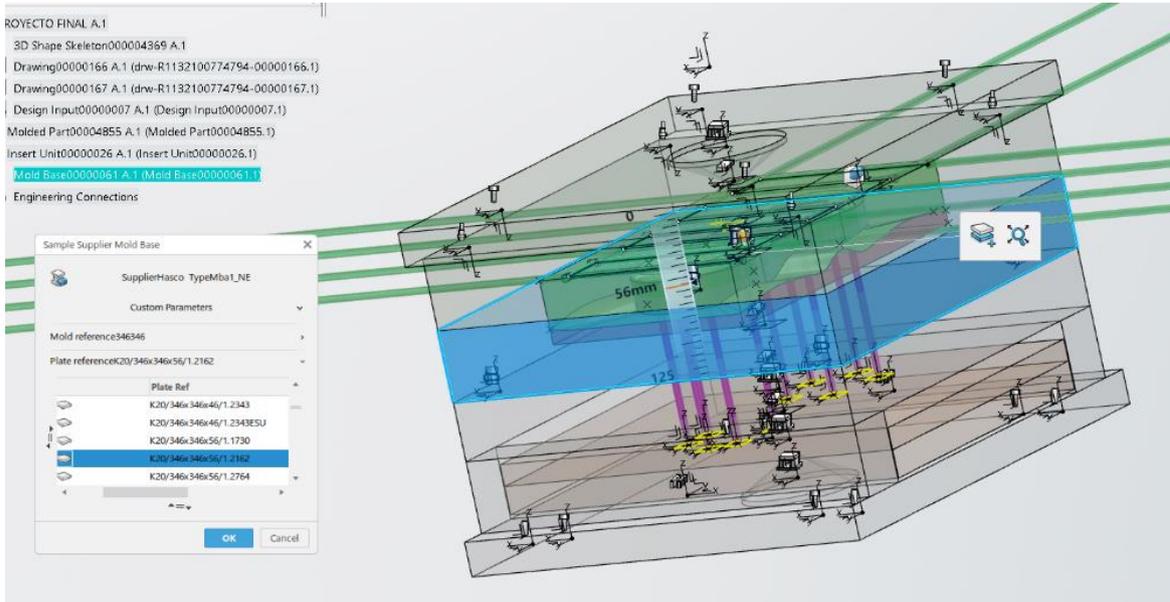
Selección de la placa de cavidad de la parte móvil.
